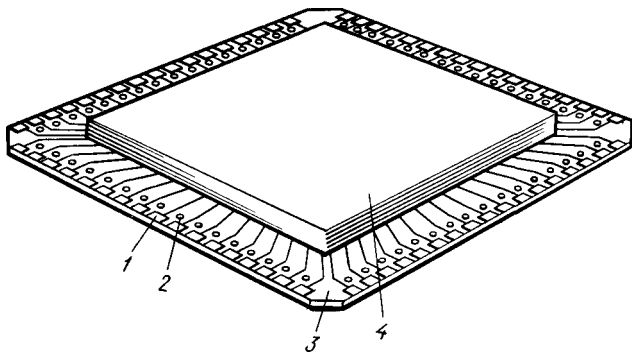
Микрокорпус с двухрядными выводами и крышкой:
